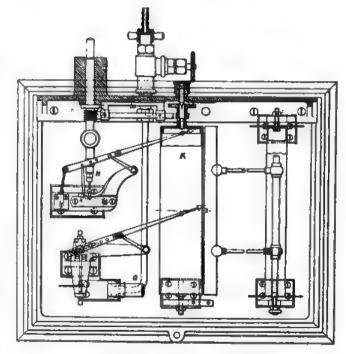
Grundriss der Registrier-Apparate.
